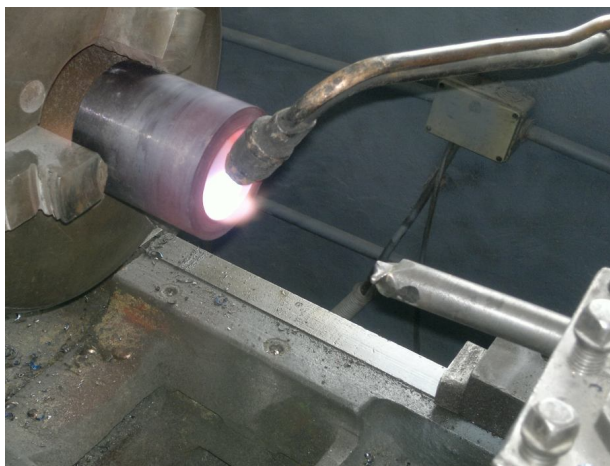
Фотография нагрева втулки перед выглаживанием внутренней цилиндрической поверхности с нагревом (инструмент – гладилка имеет сферическую контактную часть из материала Т5К10, втулка из стали)
